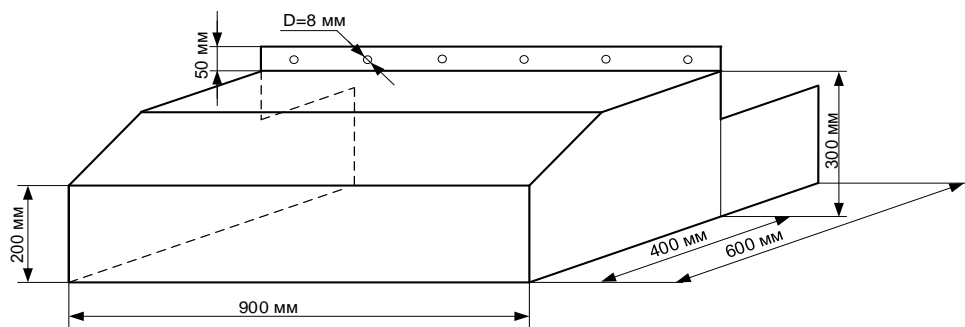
Размеры детали (Кожух защитный ТС ТМ 160,250)
